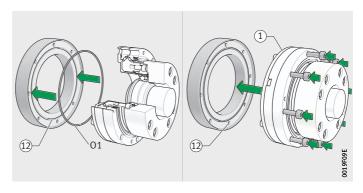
将 0 型圈 01 和柔性齿轮安装在相 邻结构上
